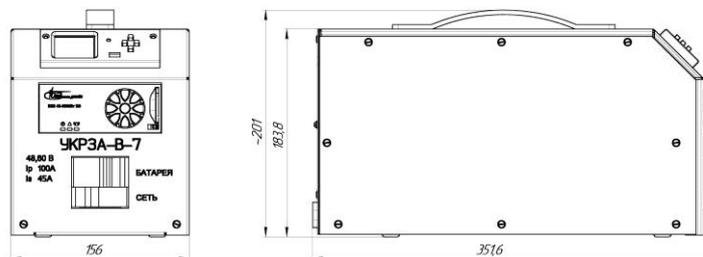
Габаритный чертеж УКРЗА-В-7
